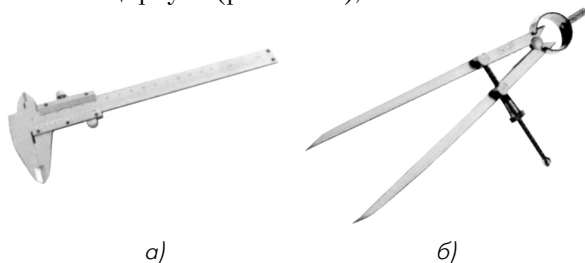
Штангенциркуль (а) и разметочный циркуль (б)
